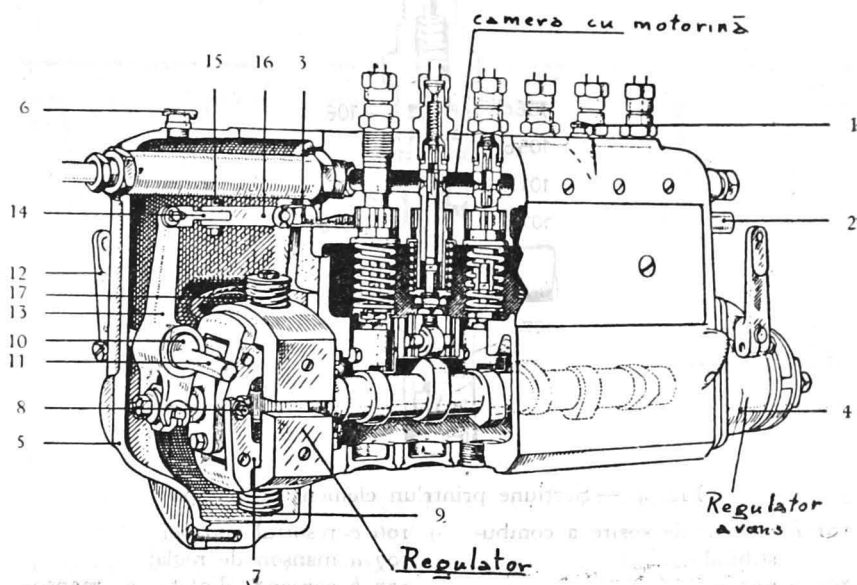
Pompa de injecție Bosch cu regulator și dispozitiv pentru reglajul avansului la injecție.
